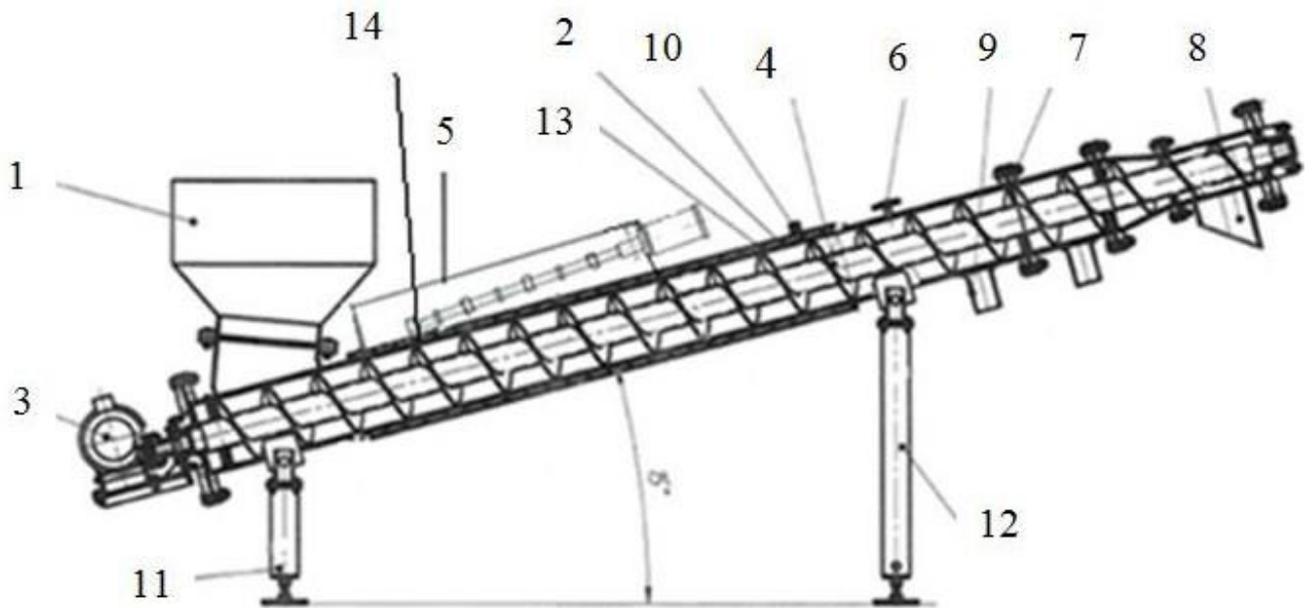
Схема ультразвукової установки для обробки зерна: 1 – бункер; 2 – корпус; 3 – мотор-редуктор; 4 – шнек; 5 – ультразвуковий випромінювач; 6 – штуцер подачі води; 7 – перфорована перегородка; 8 – вивантажний патрубков; 9 – патрубков з сіткою для відведення води; 10 – датчик температури; 11 – нерухома стійка; 12 – регульована стійка; 13 – кабельний нагрівач; 14 – захисний екран з утеплювачем
